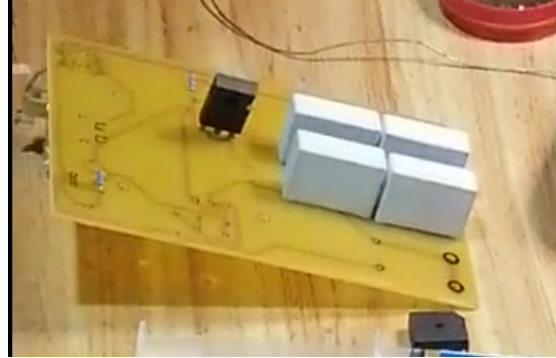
Montaje del circuito para soldado de componentes.
